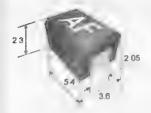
Внешний вид и размеры корпуса DO-214AA
